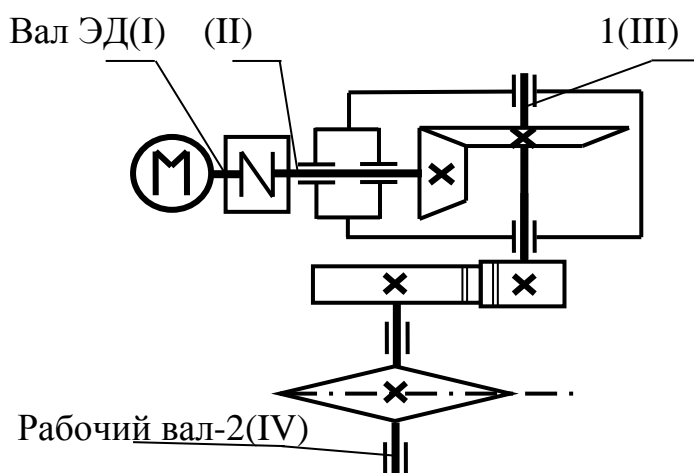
Образец схемы привода с открытой цилиндрической передачей
